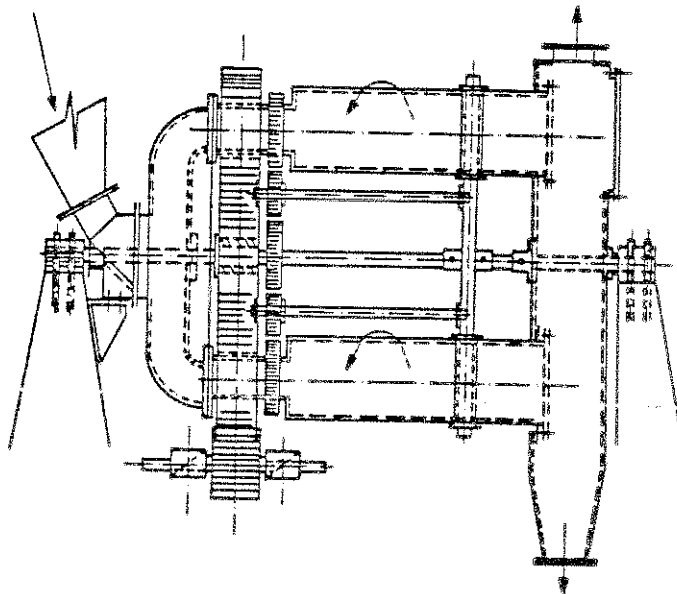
Prinzipskizze einer Planeten-Kugelmühle für Trockenmahlung
